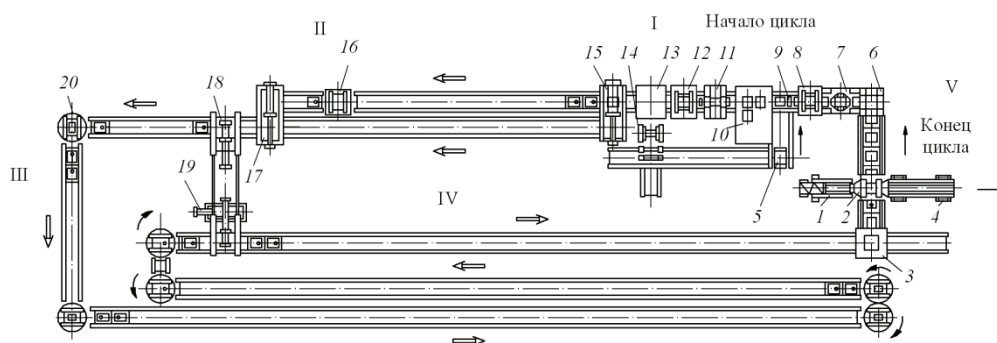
Планировка линии модели Л651: 1 – сталкиватель; 2 – пресс выбивки; 3 – съемщик залитых форм; 4 – решетка выбивная; 5 – стол подъемный; 6 – распаровщик; 7 – механизм очистки опок; 8 – кантователь опок низа; 9 – механизм сборки; 10 – дозатор; 11 – пресс дифференциальный; 12 – кантователь полуформ; 13 – механизм вытяжки; 14 – кантователь моделей; 15 – тележка передаточная; 16 – кантователь полуформ верх; 17 – сборщик форм; 18 – перекладчик грузов и поддонов; 19 – механизм очистки поддонов; 20 – стол поворотный. Участки линии:
